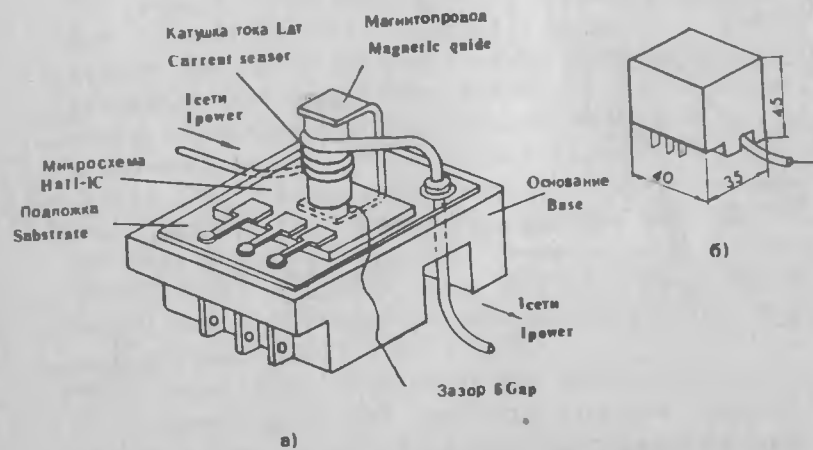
Датчик максимального тока: а - эскиз конструкции; б - габариты;
